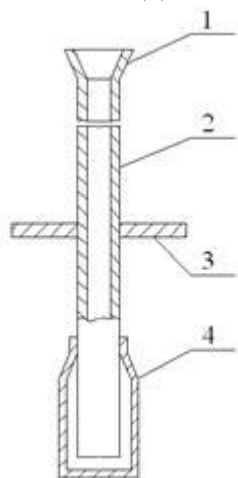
Установка переливной трубы: 1 – конус; 2 – труба; 3 – тарелка; 4 – стакан
